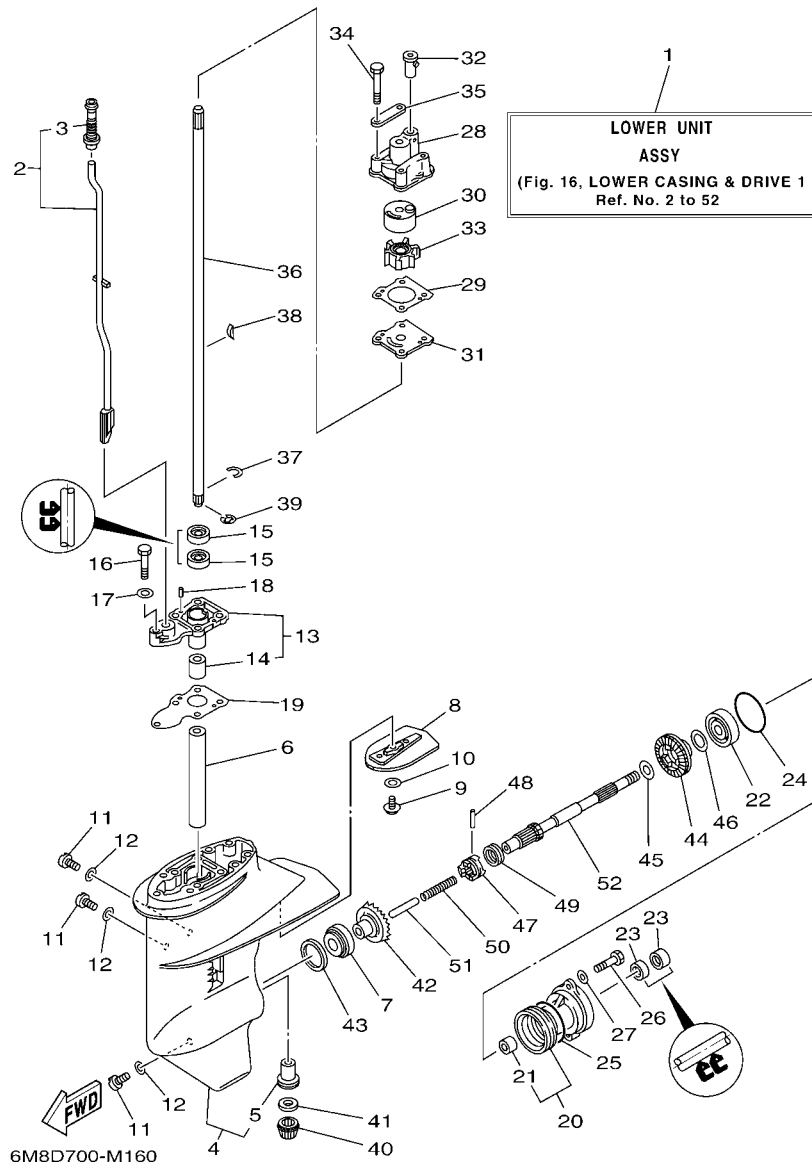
LOWER CASING & DRIVE 1 CARCACA INF. E TRANSMISSAO 1
